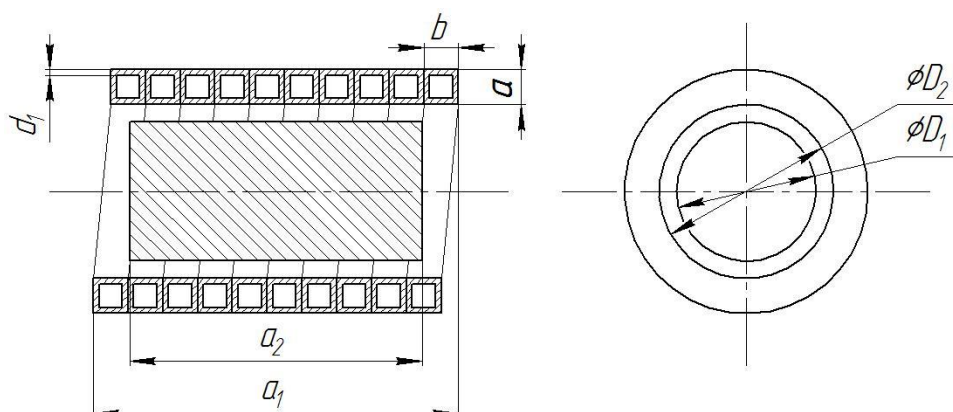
Катушка индуктора, охватывающая нагреваемую деталь
